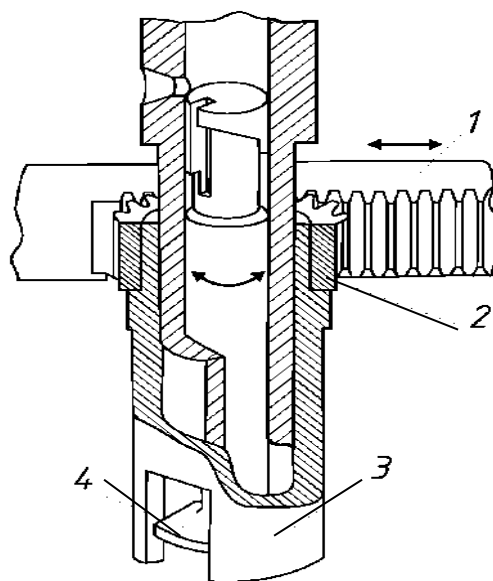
зубчасто-рейкова передача для повертання плунжера: 1 - зубчаста рейка; 2 - зубчастий сектор; 3 - втулка; 4 - хвостовик плунжера
